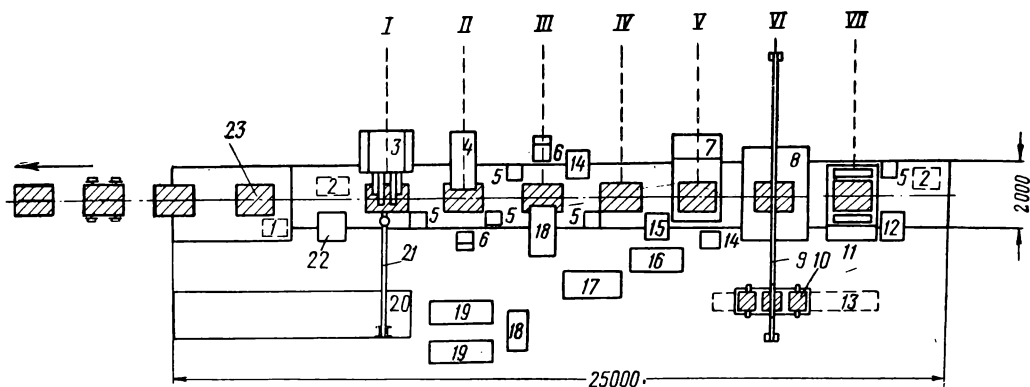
Схема конвейера для сборки тяговых двигателей и его оснащение:
